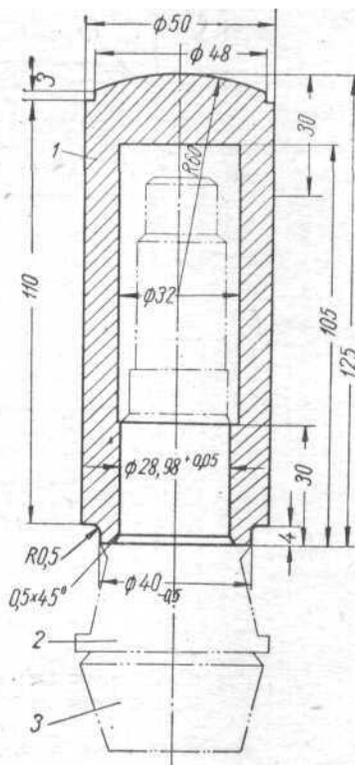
Оправка для напрессовывания внутреннего кольца заднего подшипника на вал ведущей шестерни главной передачи:
